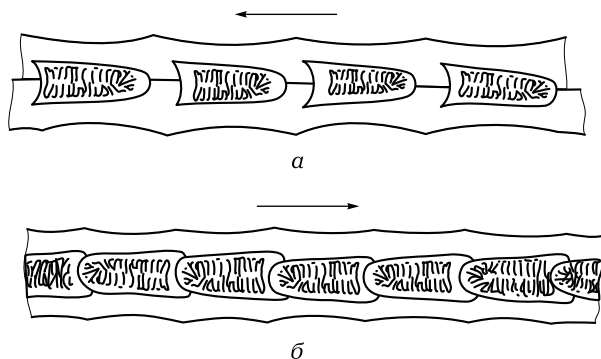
Схема структуры шовно-сварного соединения:
